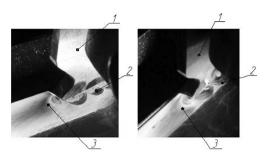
Процесс резания: 1 – резец, 2 – след элементарного скола, 3 – поле напряжений
